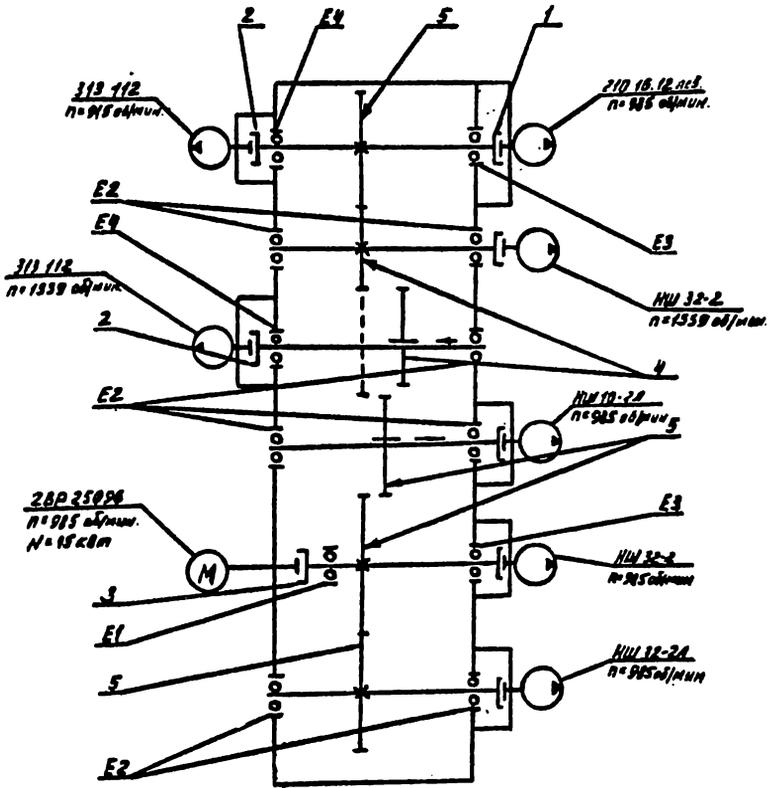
Кинематическая схема редуктора гусеничного хода :
